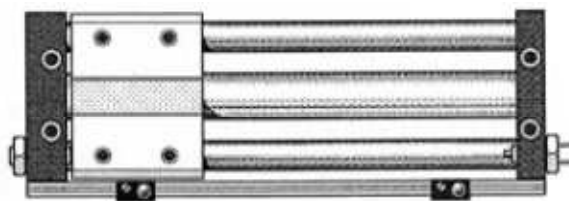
Spojení suportu s poháněným mechanismem[1]
